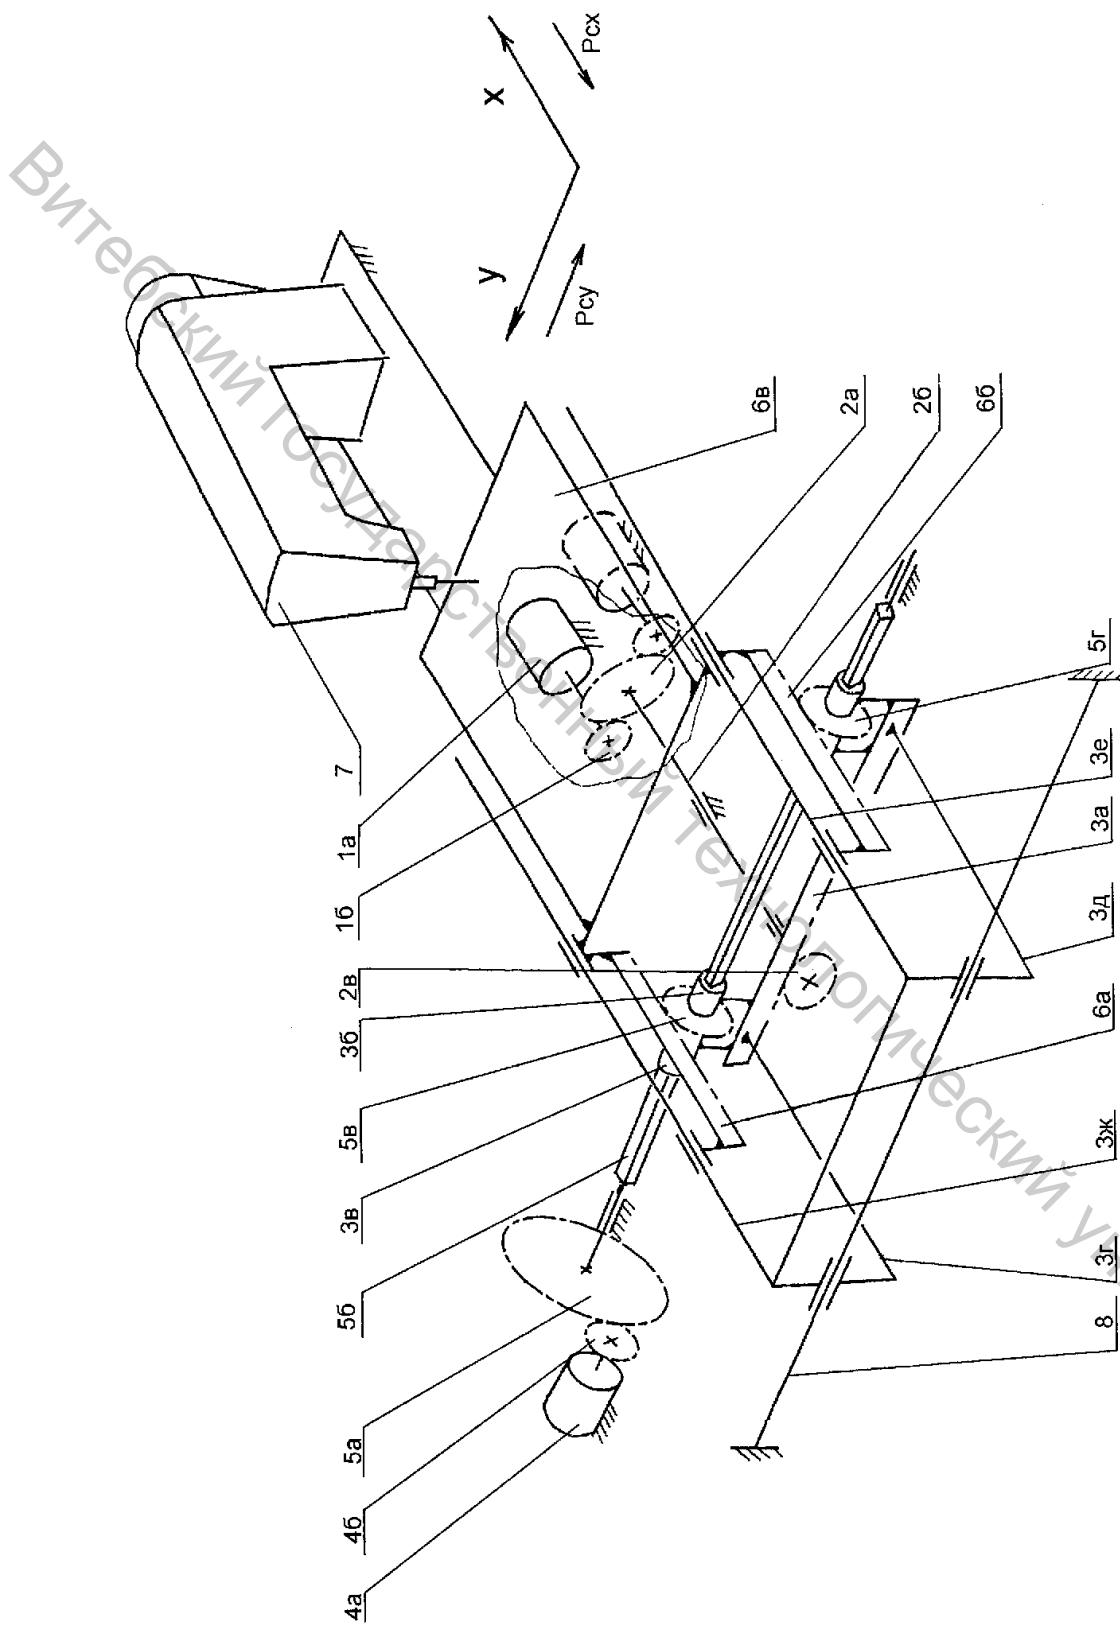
Кинематическая схема координатного устройства полуавтомата для сборки заготовки верха обуви
